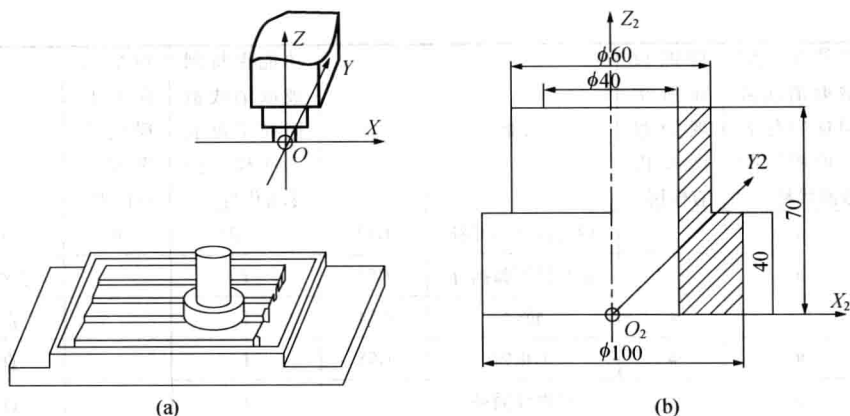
立式数控铣床坐标系和机床原点、工件原点
